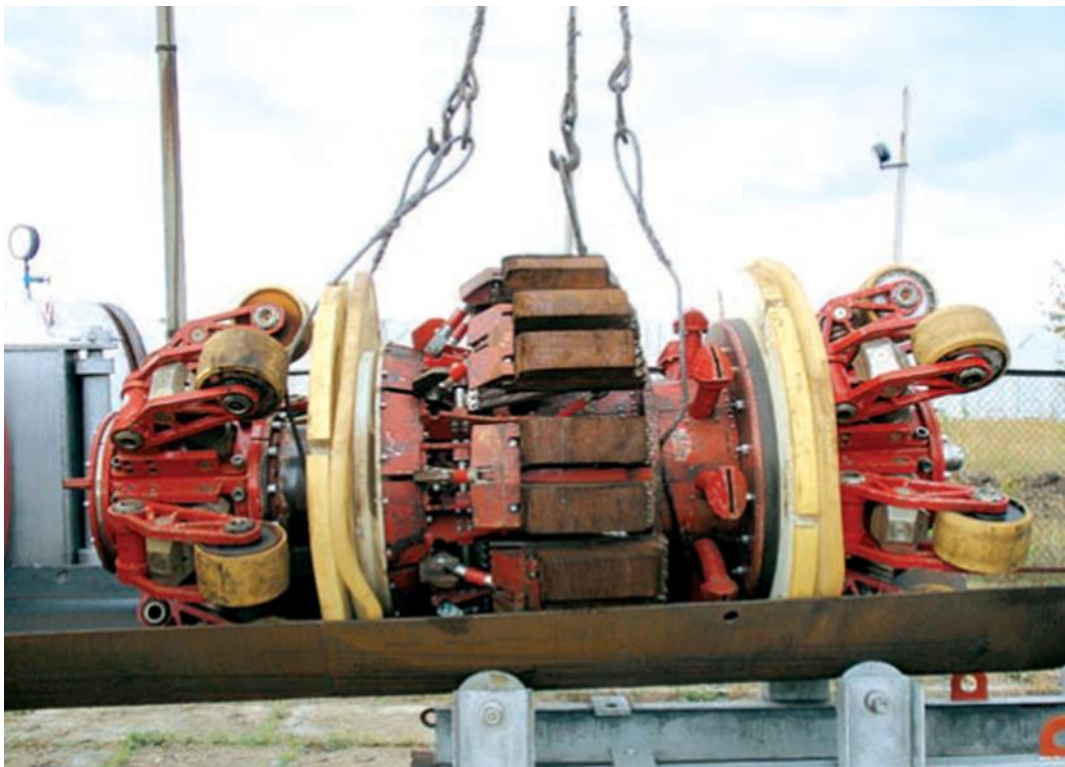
Інжекційний очисний поршень з направляючими опорними роликками
